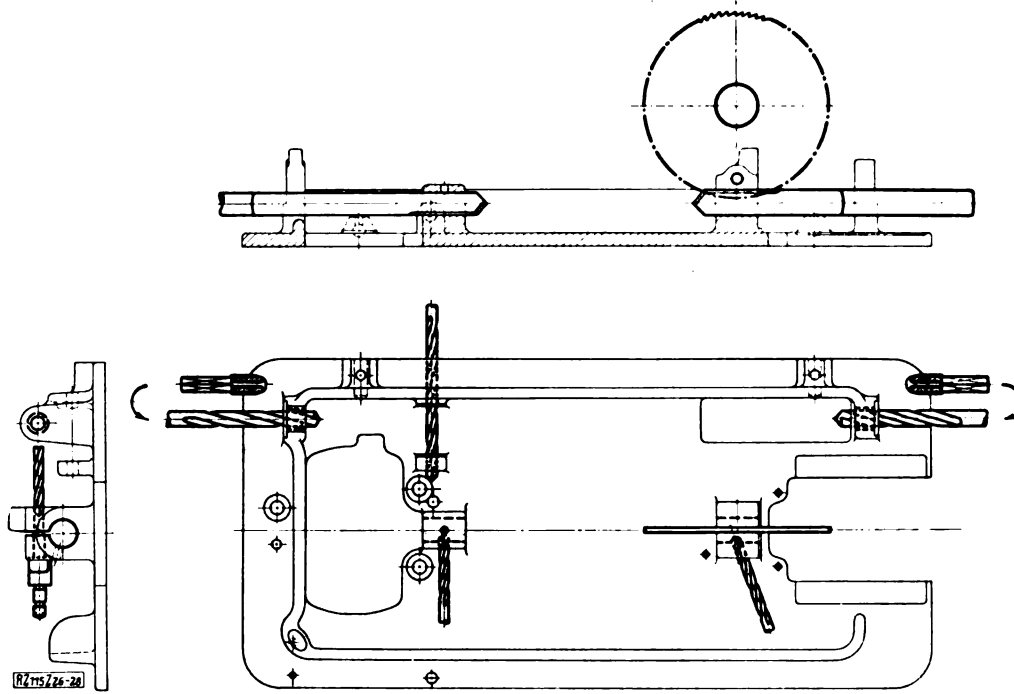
bis 28. Nähmaschinen-Grundplatte, zweite Arbeitsstufe auf Sondermaschine, Abb. 25 (Textbl. 1), für Bohrungen, Fräsungen, Gewindeschneiden und Schlitten.
